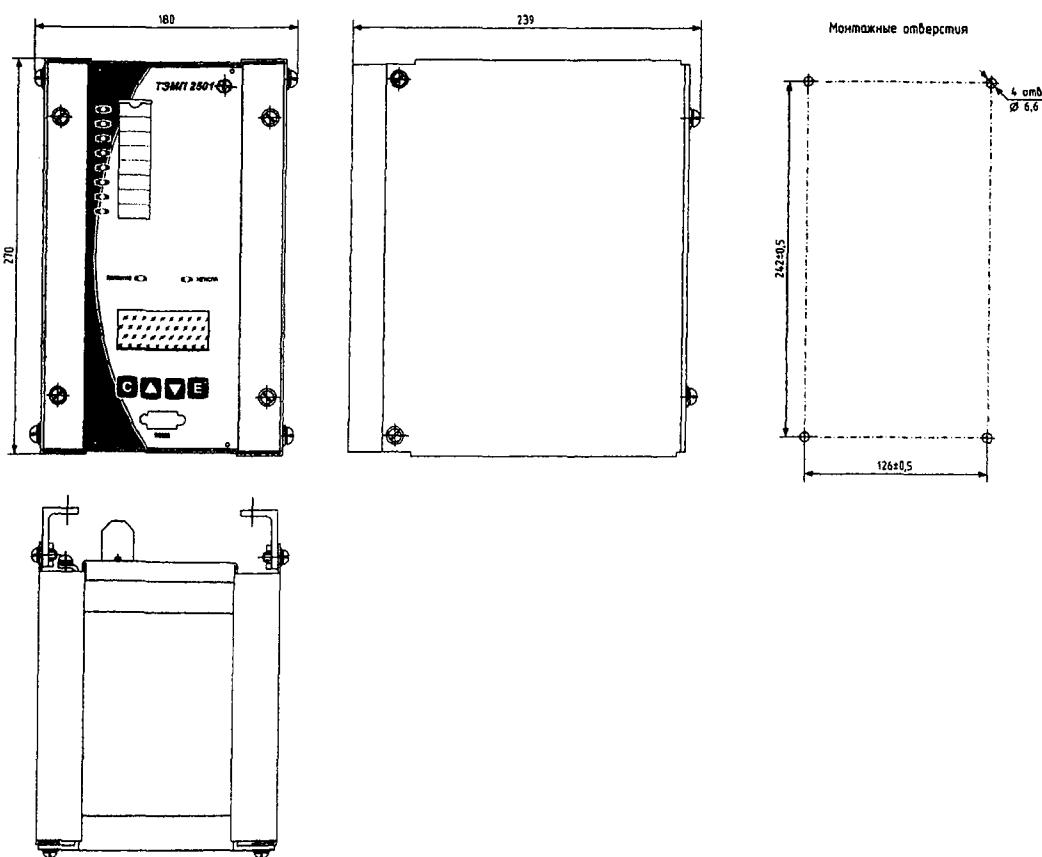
Габаритные и установочные размеры ТЭМП 2501-52/62
